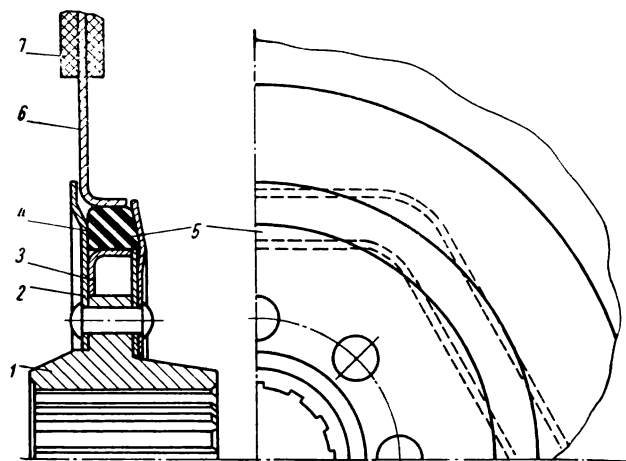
Схема расположения окон и упора гасителя колебаний:
